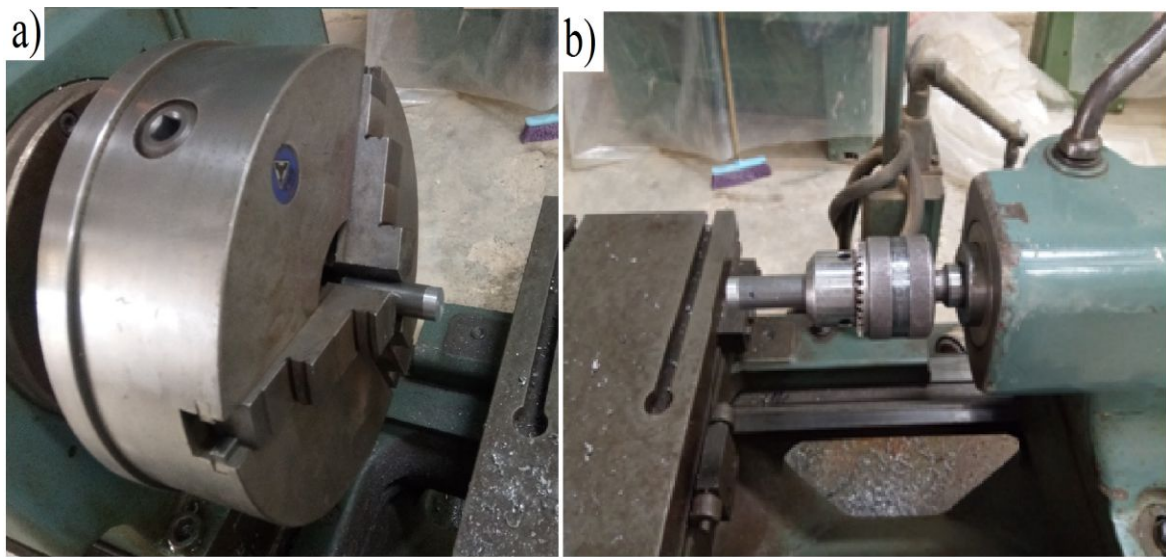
Mode de fixation des deux pièces. (a) la pièce en rotation au mandrin. (b) la pièce est fixe à la poupée mobile.
